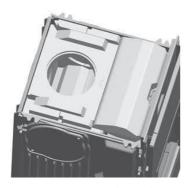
Pose de la pierre avant (H2.1-09).
